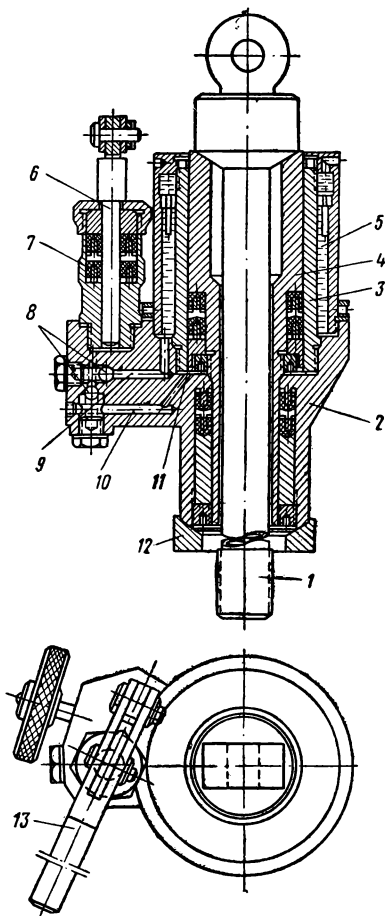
Гидравлический домкрат для запрессовки подшипниковых щитов в остов двигателя:
